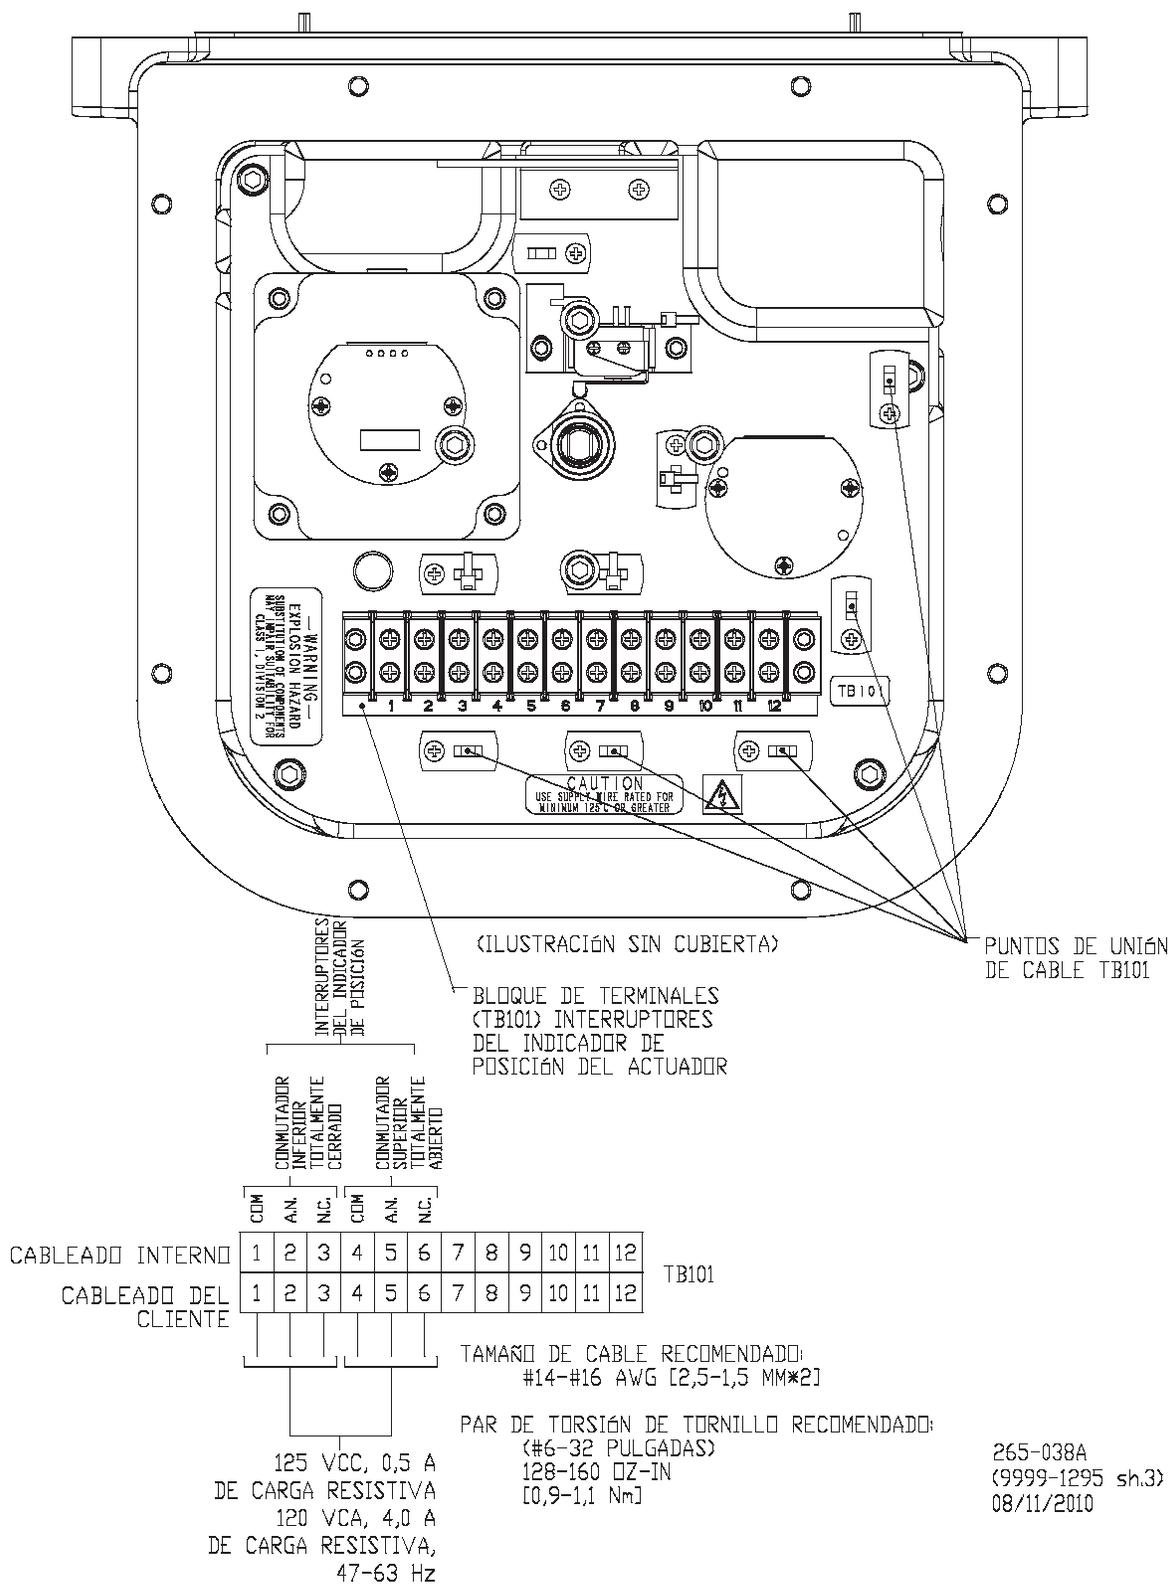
Diagrama de cableado del actuador de RVP-200 (caja de engranajes)
